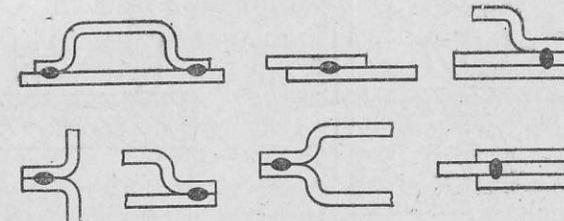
Типы сварных соединений точечной сварки
